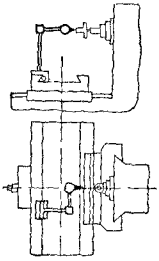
Проверка перпендикулярности направляющих станины к оси шпинделя у горизонтально-фрезерного станка при помощи устанавливаемой линейки.
